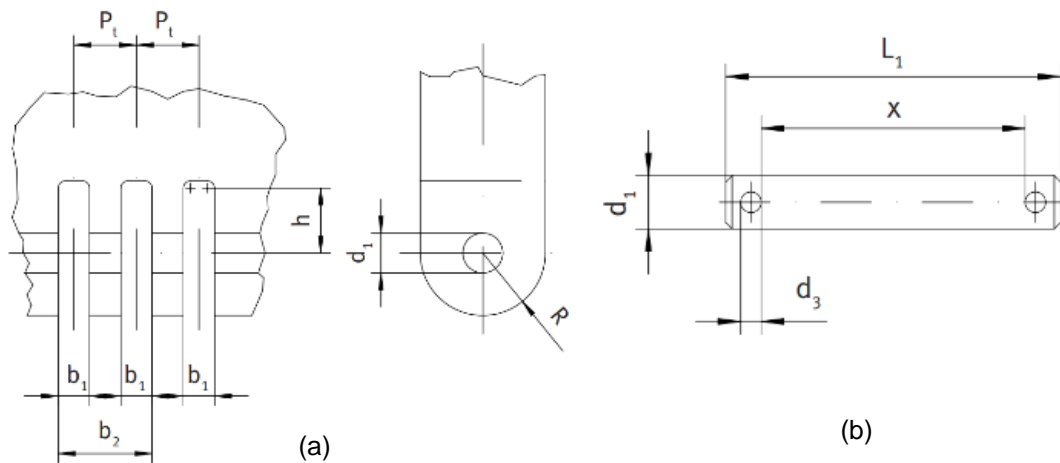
Dimensiones: a) Horquilla; b) Rodillo
